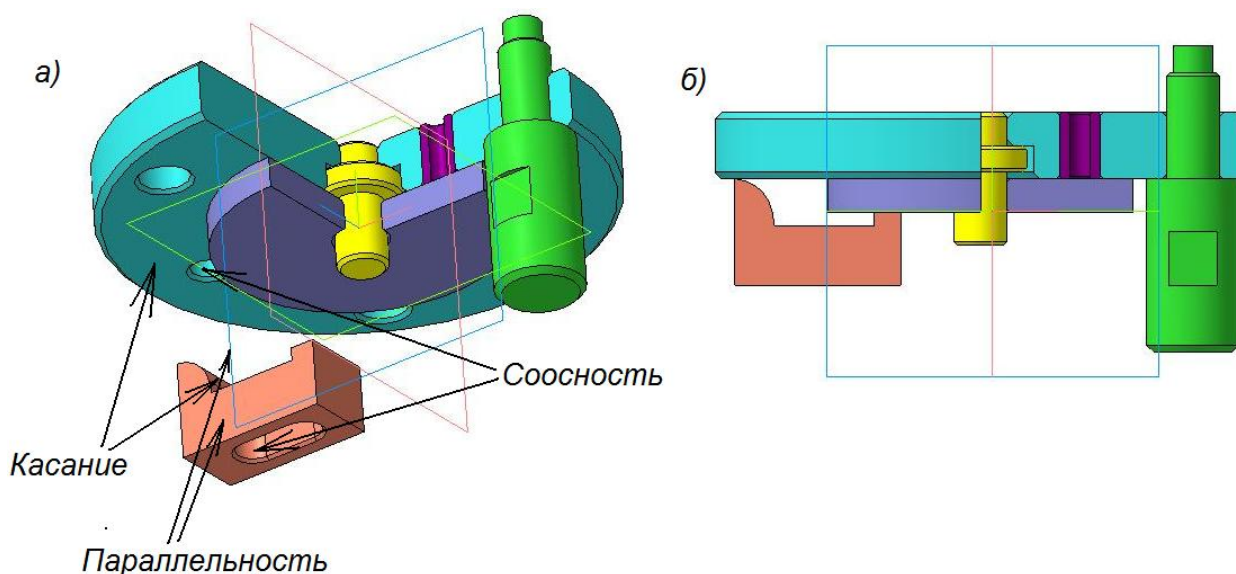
Схема выполнения сопряжений звена «Плита, заготовка – Прижим»
